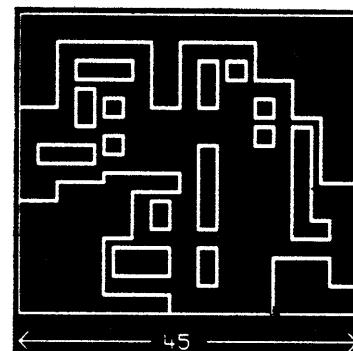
Rozložení součástek oscilátoru (zemnici fólie propojena se stínícím krytem)
